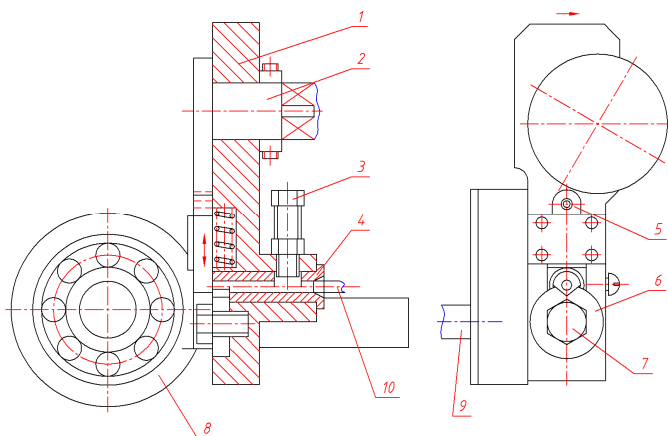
Пристрій для навивання пружин різних типорозмірів
